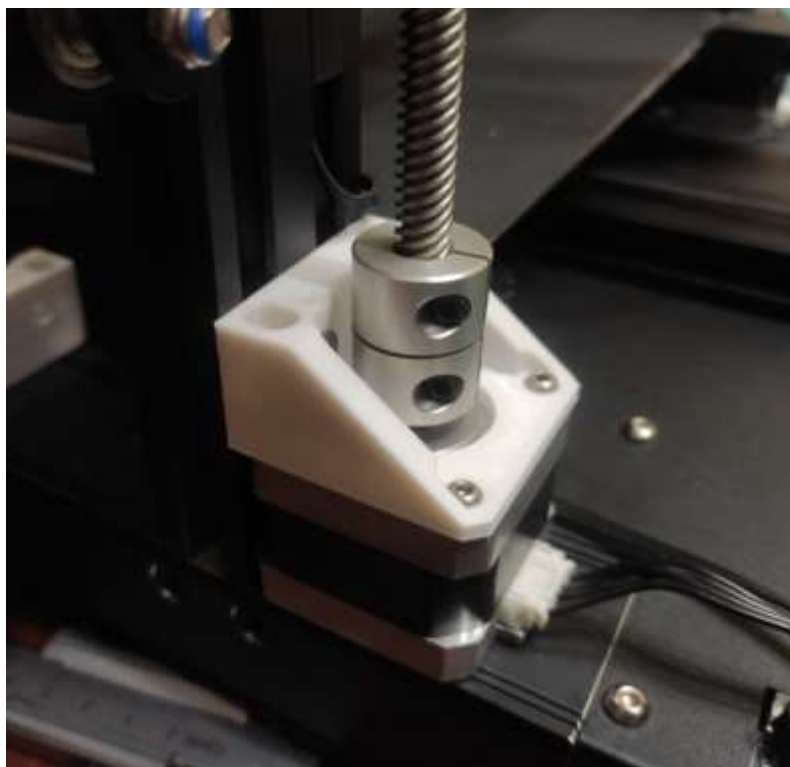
Установленное в рабочее положение крепление шагового двигателя
